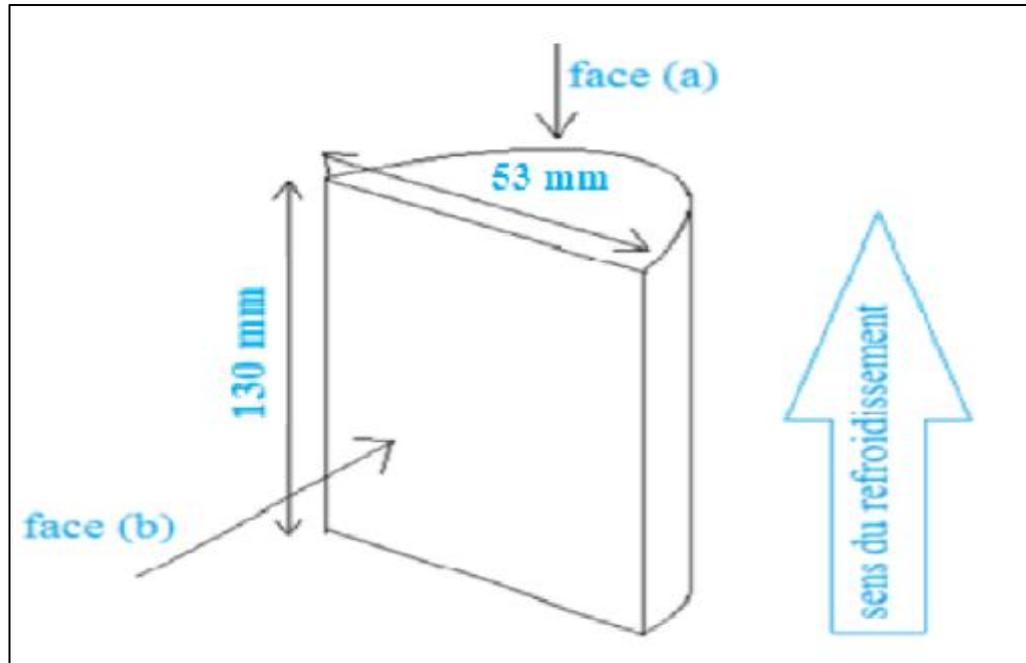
Forme, dimension (mm) et plans de découpe des échantillons.
